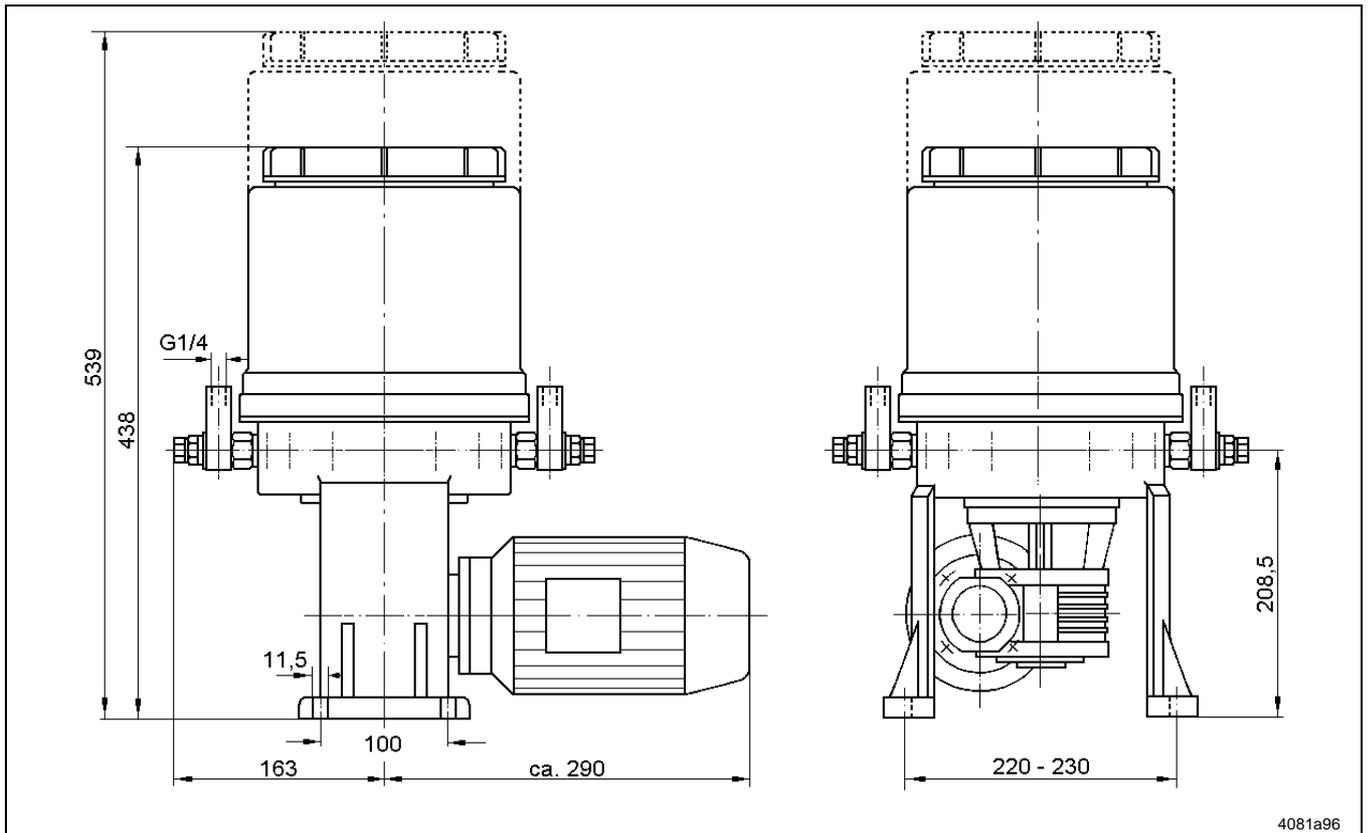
Maßzeichnung für Pumpe P 215 - M100 / M049 - 4XN / 8XN
